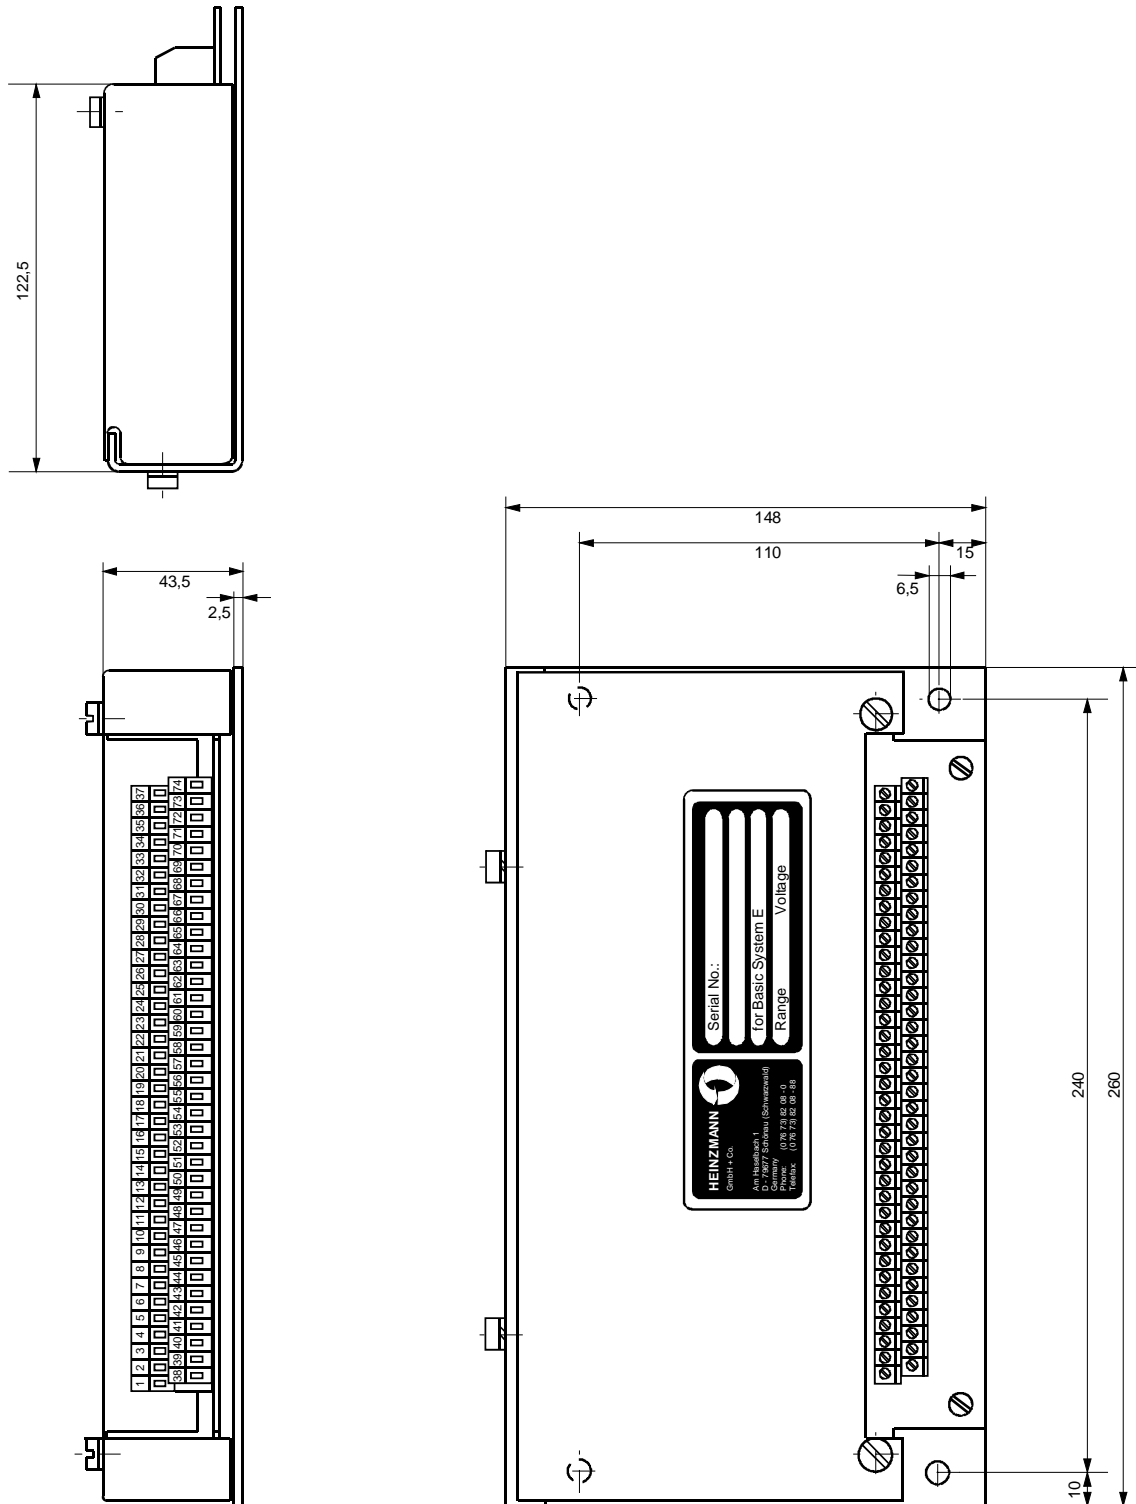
Gehäuse von DC EDC 2 - 01 - 00
